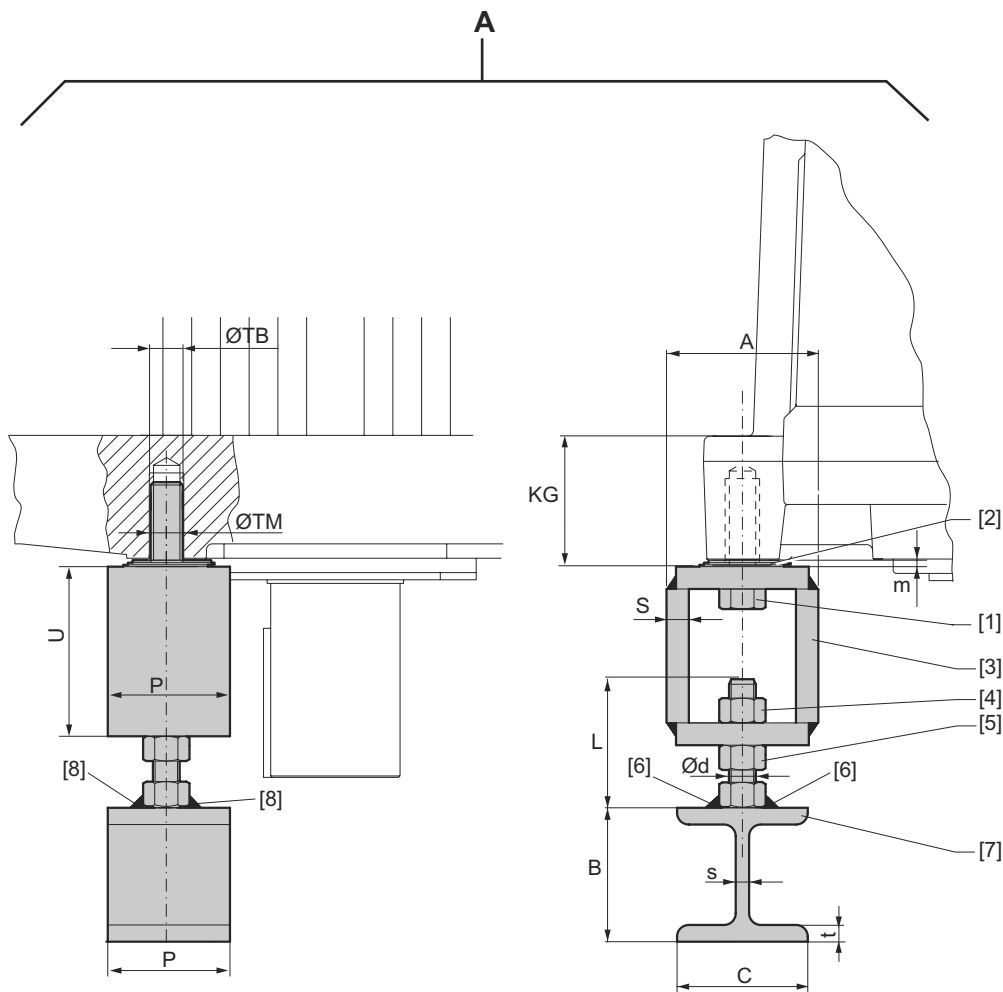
Bewehrung des Grundgusses (Pos. "A") M.V.. 10...50
